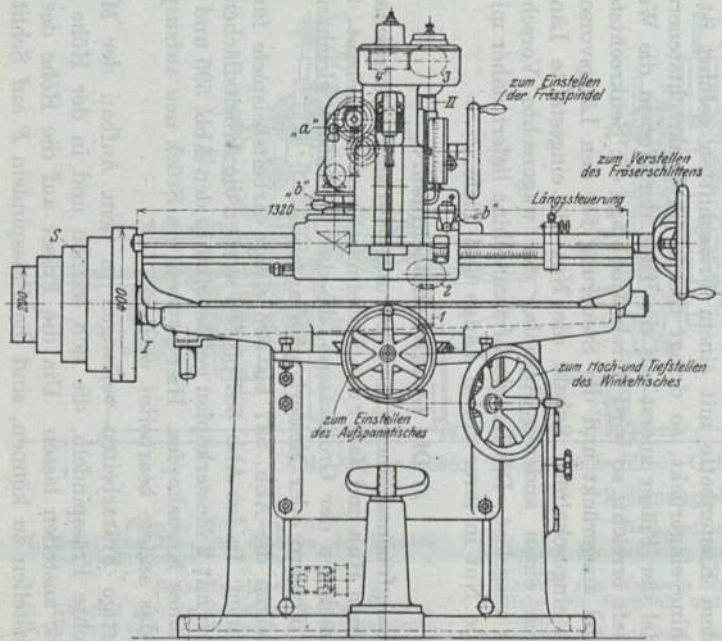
und 584. Langlochfräsmaschine. de Fries & Co., A. G., Düsseldorf.
